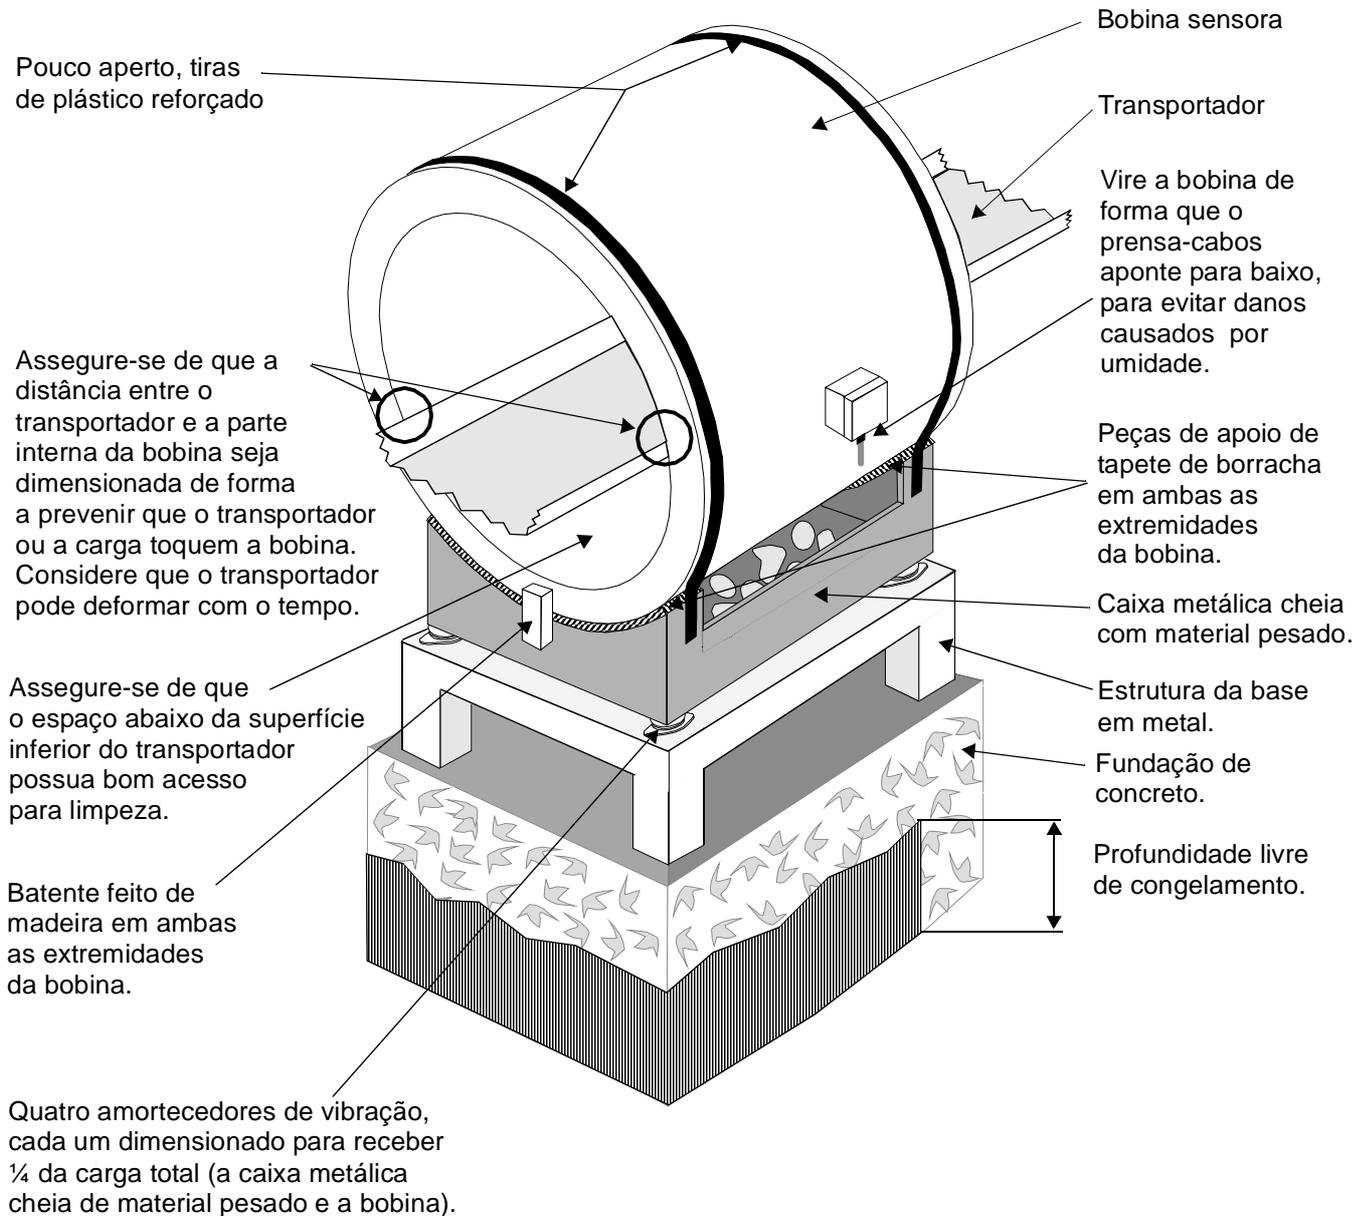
A bobina sensora montada em suporte sobre fundação.
